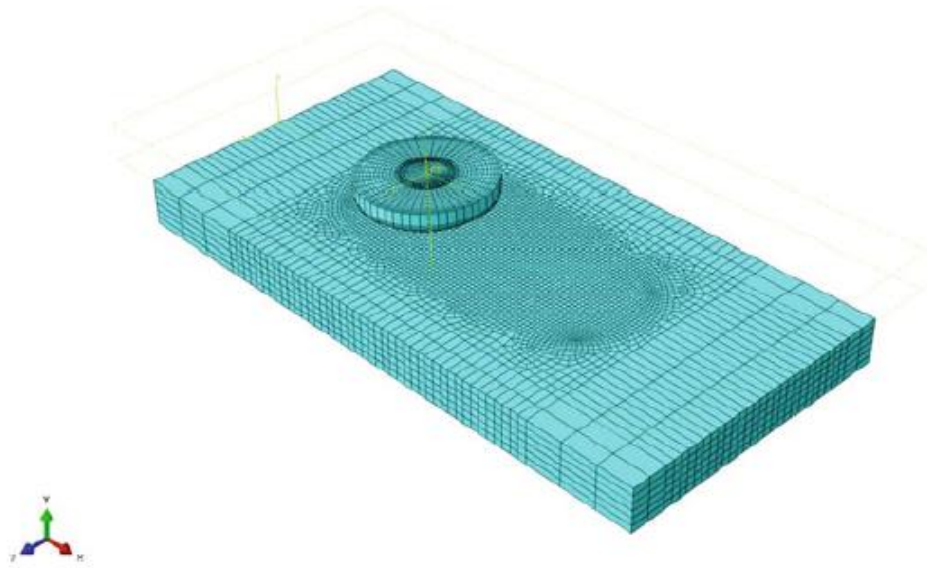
КЕ модель зварного з'єднання при ЗТП [6]
